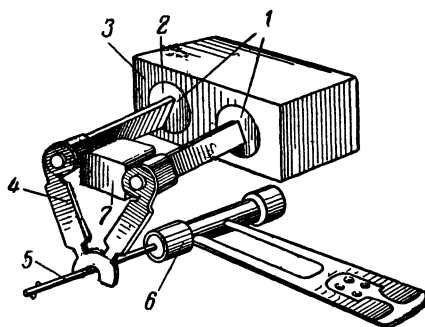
Устройство пьезокерамической двухбалочной головки типа 9ТА.
